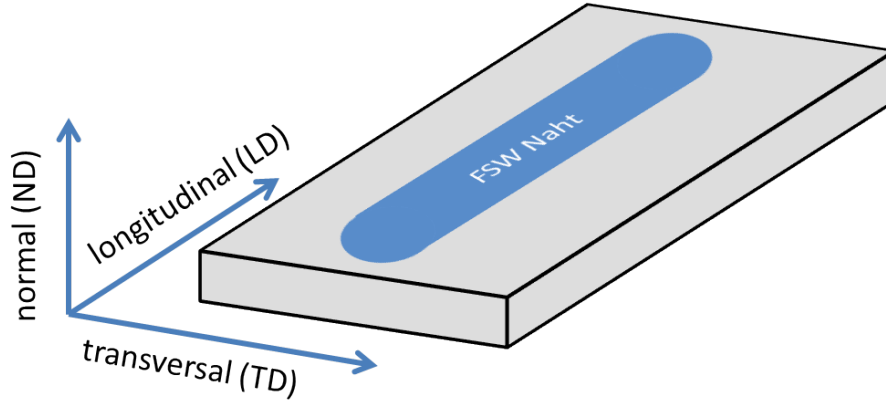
Richtung der Eigenspannungen im Bezug zur Schweißnaht. Die Longitudinalrichtung zeigt in Schweißrichtung, die Transversalrichtung steht senkrecht zu ihr, parallel zur Probenoberfläche. Die Normalenrichtung steht senkrecht auf der Probenoberfläche.
